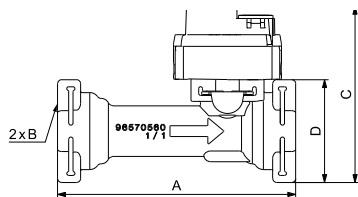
Abmessungen des Sensors VFS 2-40 l/min (ohne Adapter)
